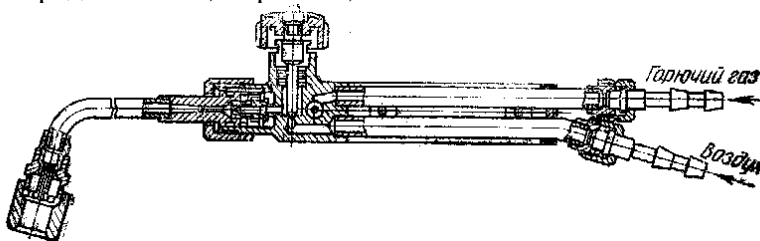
Горелка ГВП-4 для газо-воздушной пайки
